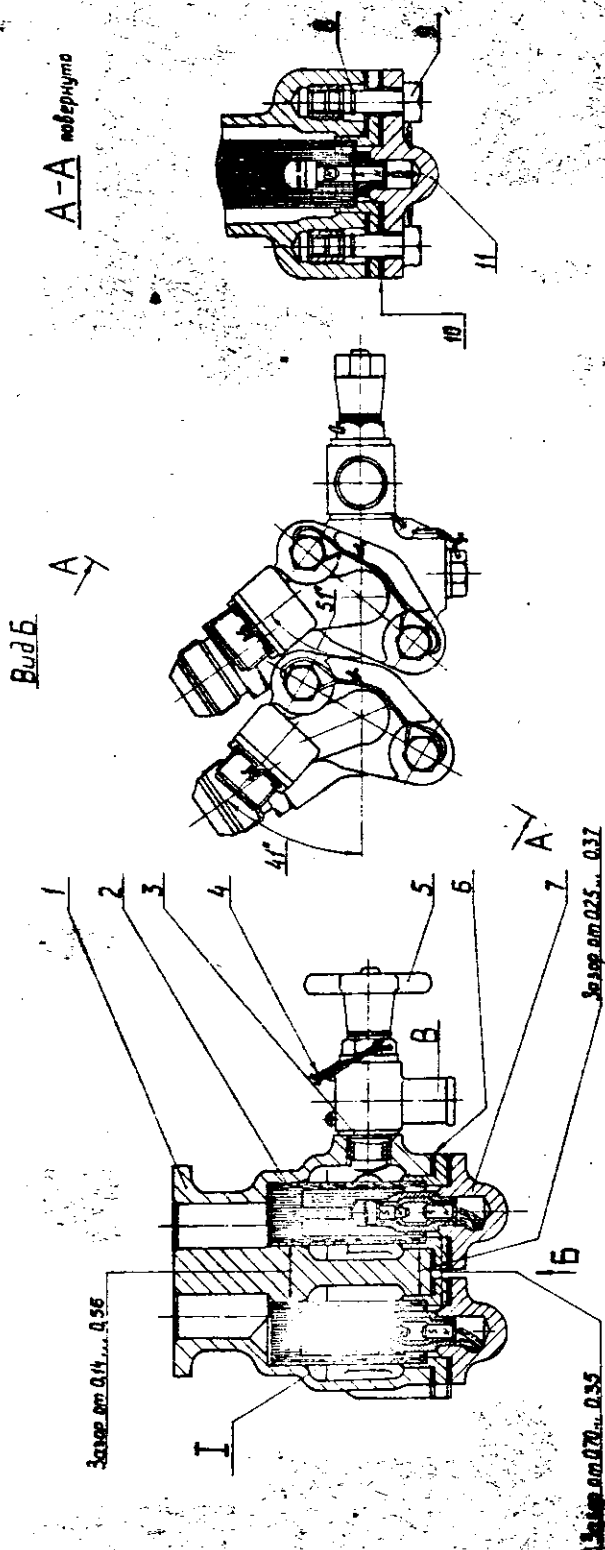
К замене корпуса масляных фильтров заднего подшипника компрессора и подшипника турбины.
